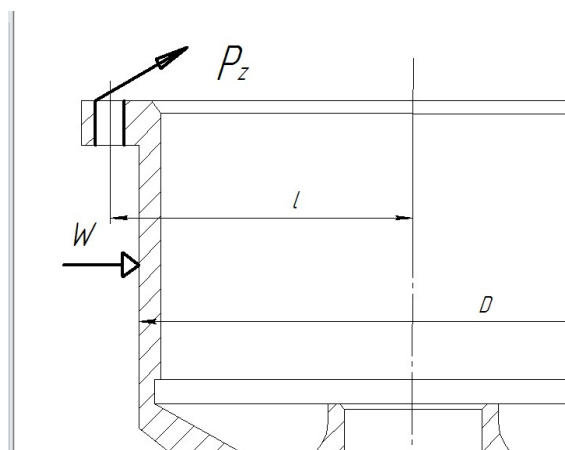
Схема базування та закріплення заготовки корпусу гідроциліндра
